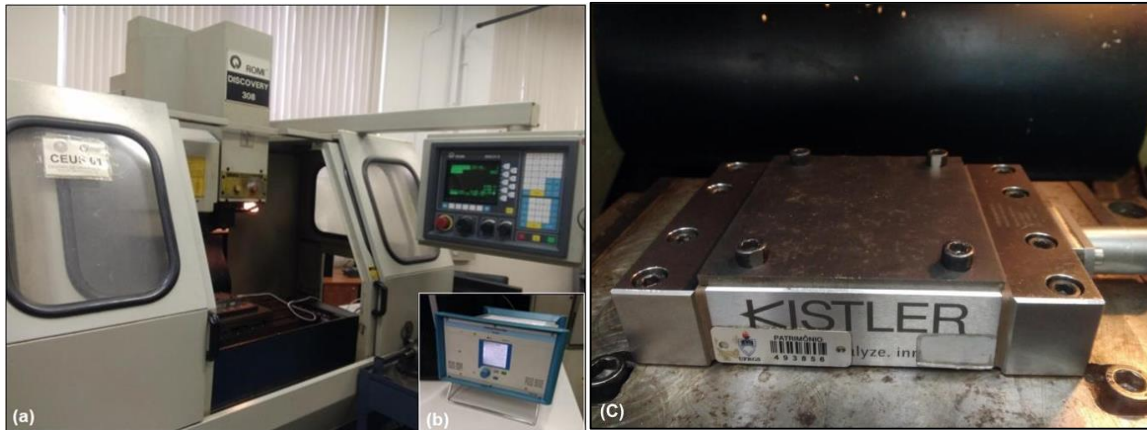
(a) Centro de usinagem Romi Discovery 308; (b) Condicionador de sinais KISTLER 5070A; (c) Dinamômetro piezelétrico Kistler<sup>®</sup>9129A com o corpo de prova fixado.
